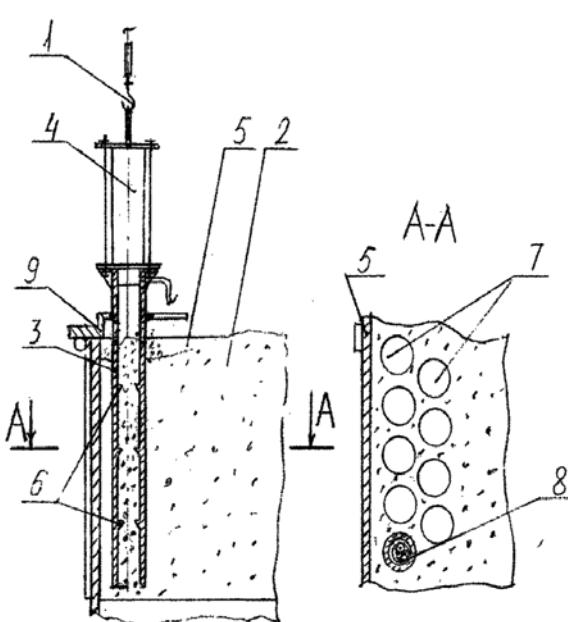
Устройство для разрушения смерзшегося груза в полувагоне: 1 – грузоподъемный механизм; 2 – груз; 3 – рабочий орган; 4 – ударный привод; 5 – полувагон; 6 – разрушающие груз элементы; 7 – цилиндрические полости; 8 – отделяемый элемент
